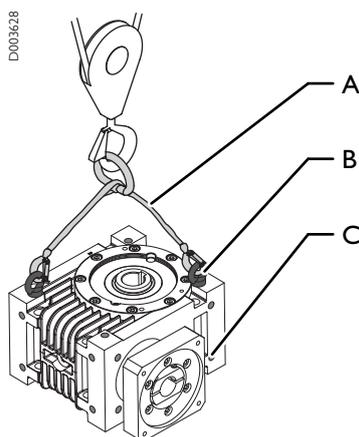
Зачаливать такелаж: Блок редуктора Güdel
